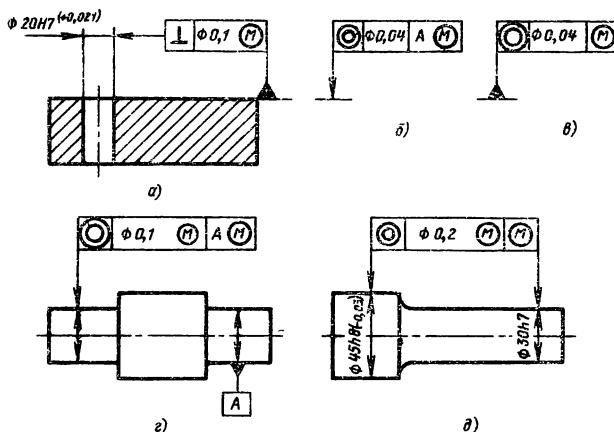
Условные знаки обозначения на чертежах зависимых допусков формы или расположения
